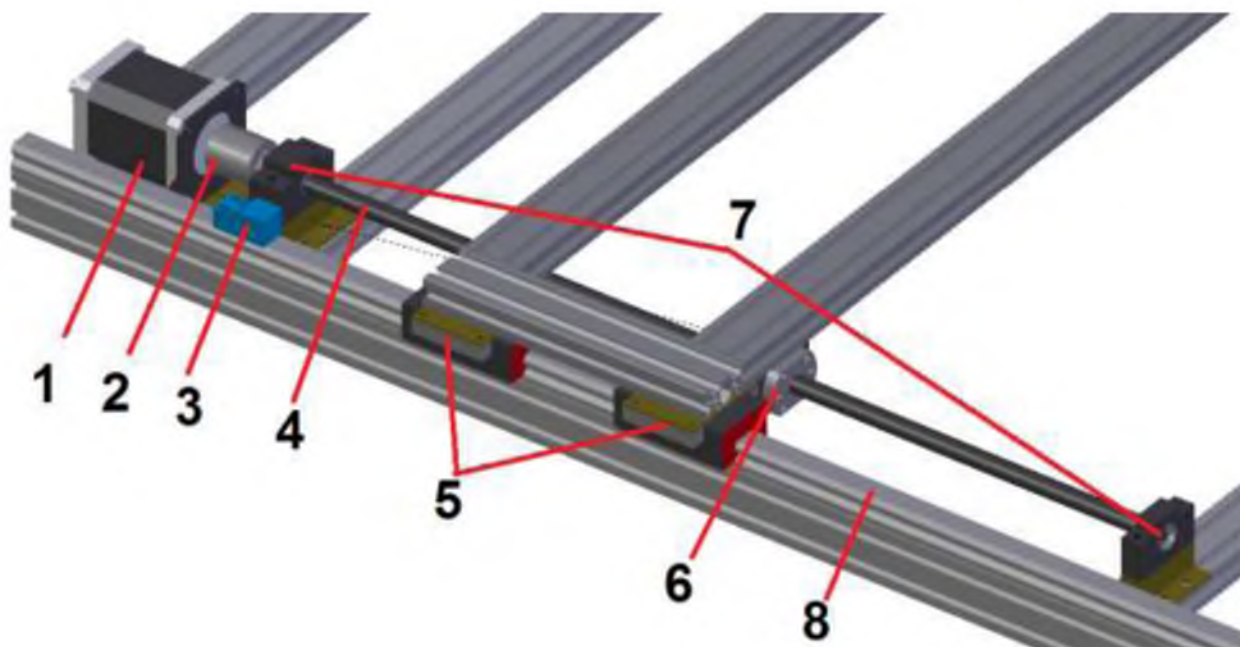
Внешний вид модуля перемещения по оси X: 1 – шаговый двигатель с креплением, 2 – соединительная муфта, 3 – бесконтактный концевой выключатель, 4 – винт ШВП, 5 – линейные модули перемещения, 6 – гайка ШВП с держателем, 7 – подшипниковые опоры ШВП, 8 – рельсовая направляющая.
